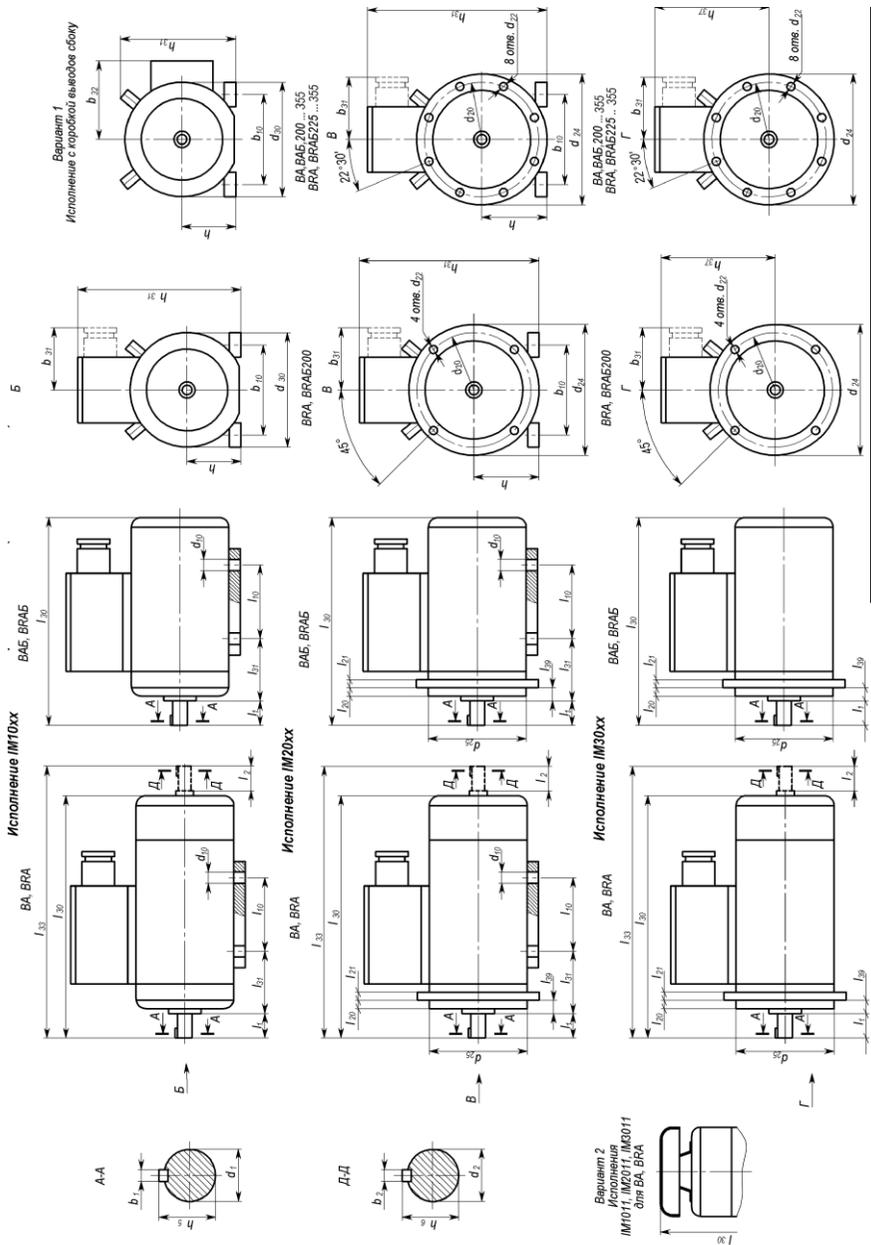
Габаритные и установочные размеры двигателей
